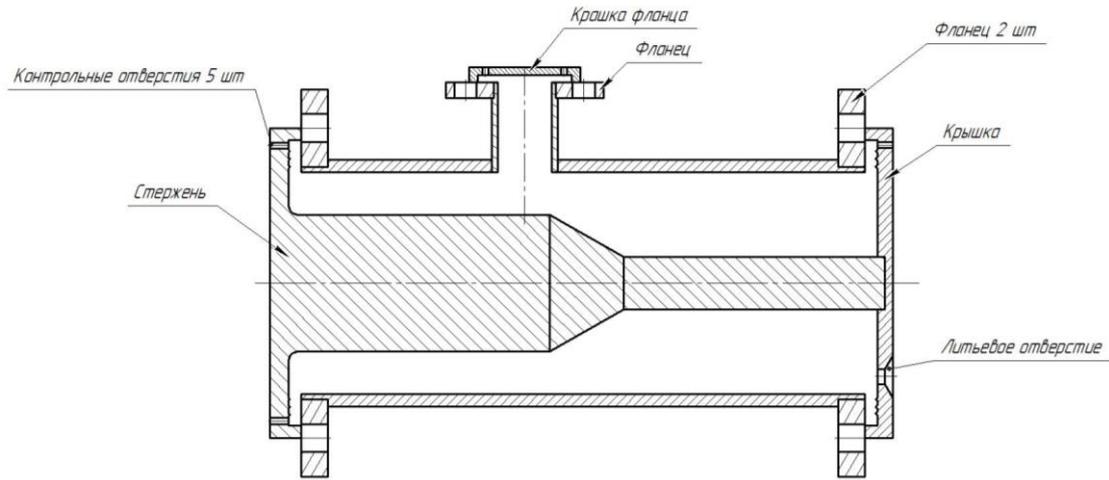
Схема сборки пресс-формы первой половины корпуса эжектора
